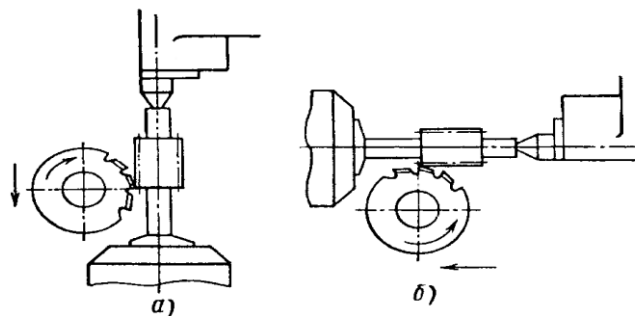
Схеми нарізування зубчастих коліс на зубофрезерних верстатах
